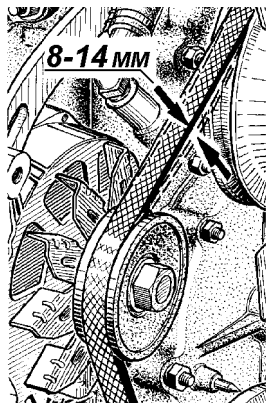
Проверка натяжения ремня вентилятора двигателей УМЗ
